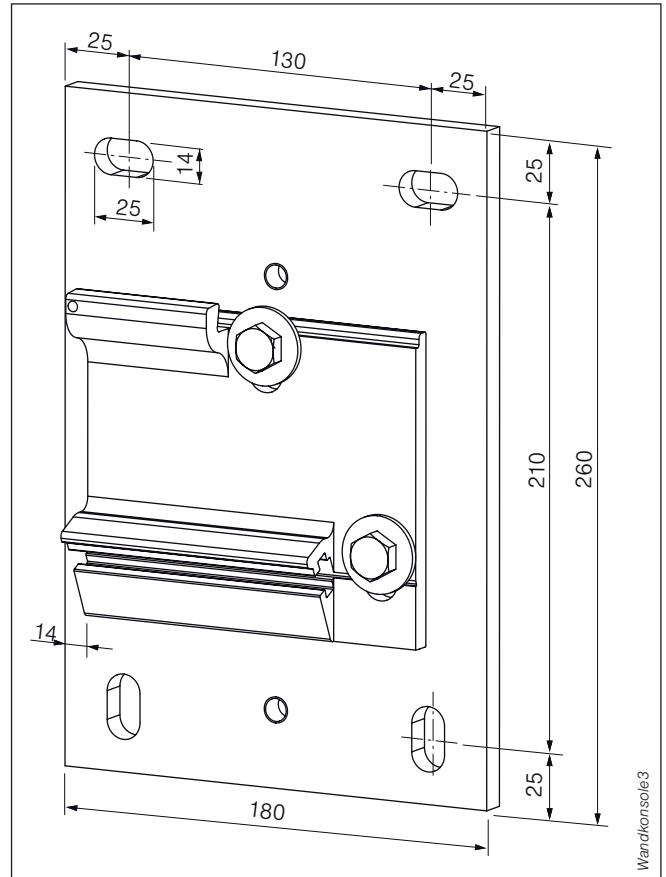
Consola tipo C – Fijación mural con placa de montaje
